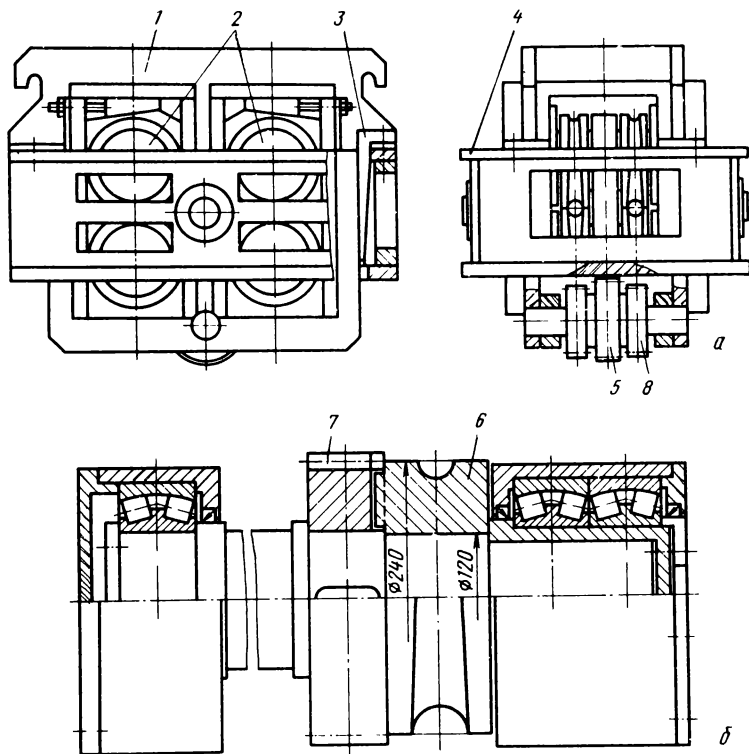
Рабочая клетка стана ХПТ 2-32:
